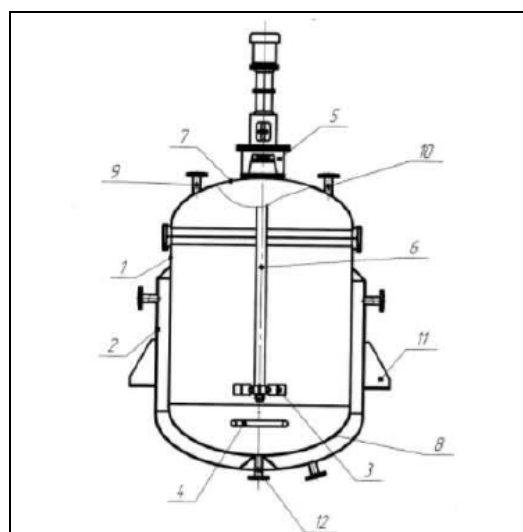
Конструкція реактора з механічним перемішувачем: 1 – корпус; 2 – сорочка; 3 – мішалка; 4 – барботер; 5 – двигун з приводом; 6 – вал мішалки; 7 – кришка; 8 – дно; 9, 10 – штуцери; 11 – опора; 12 – штуцер зливу продукту
